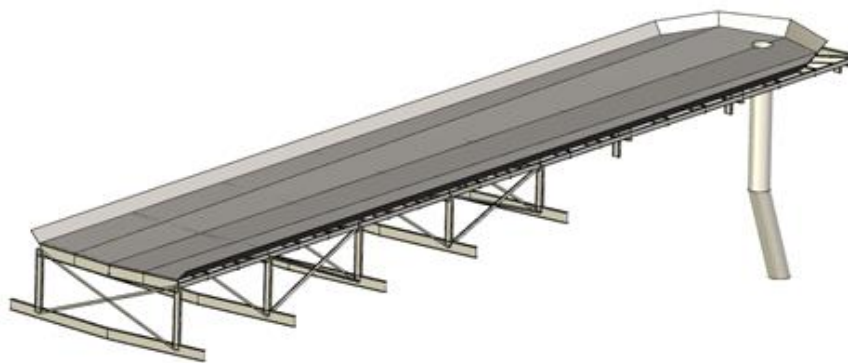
Detalhe da estrutura da calha fixa sob o carro – modelo CAD 3D.
